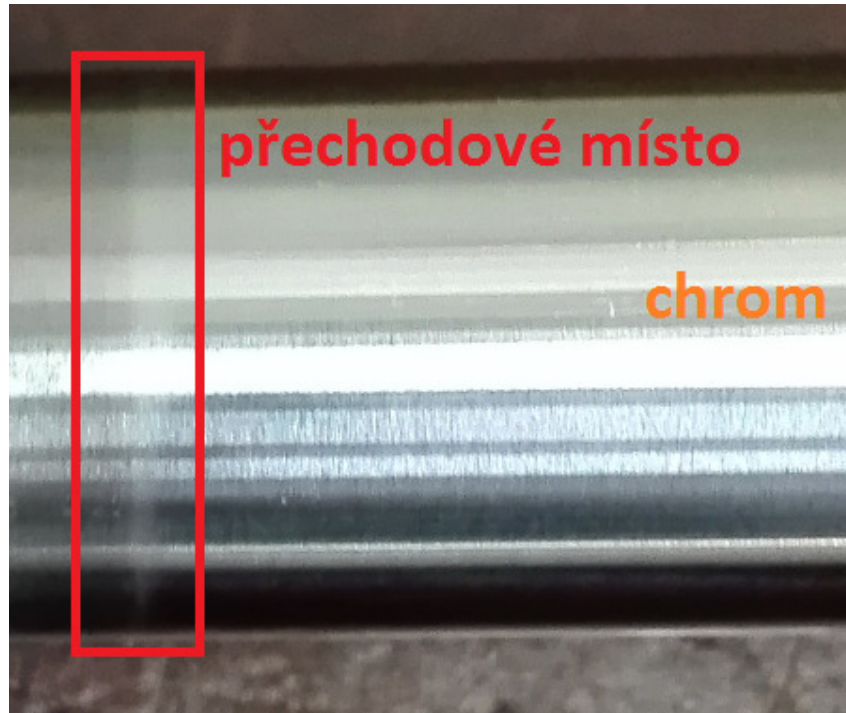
Test statického tečení po superfiniši (Vyhovující)
